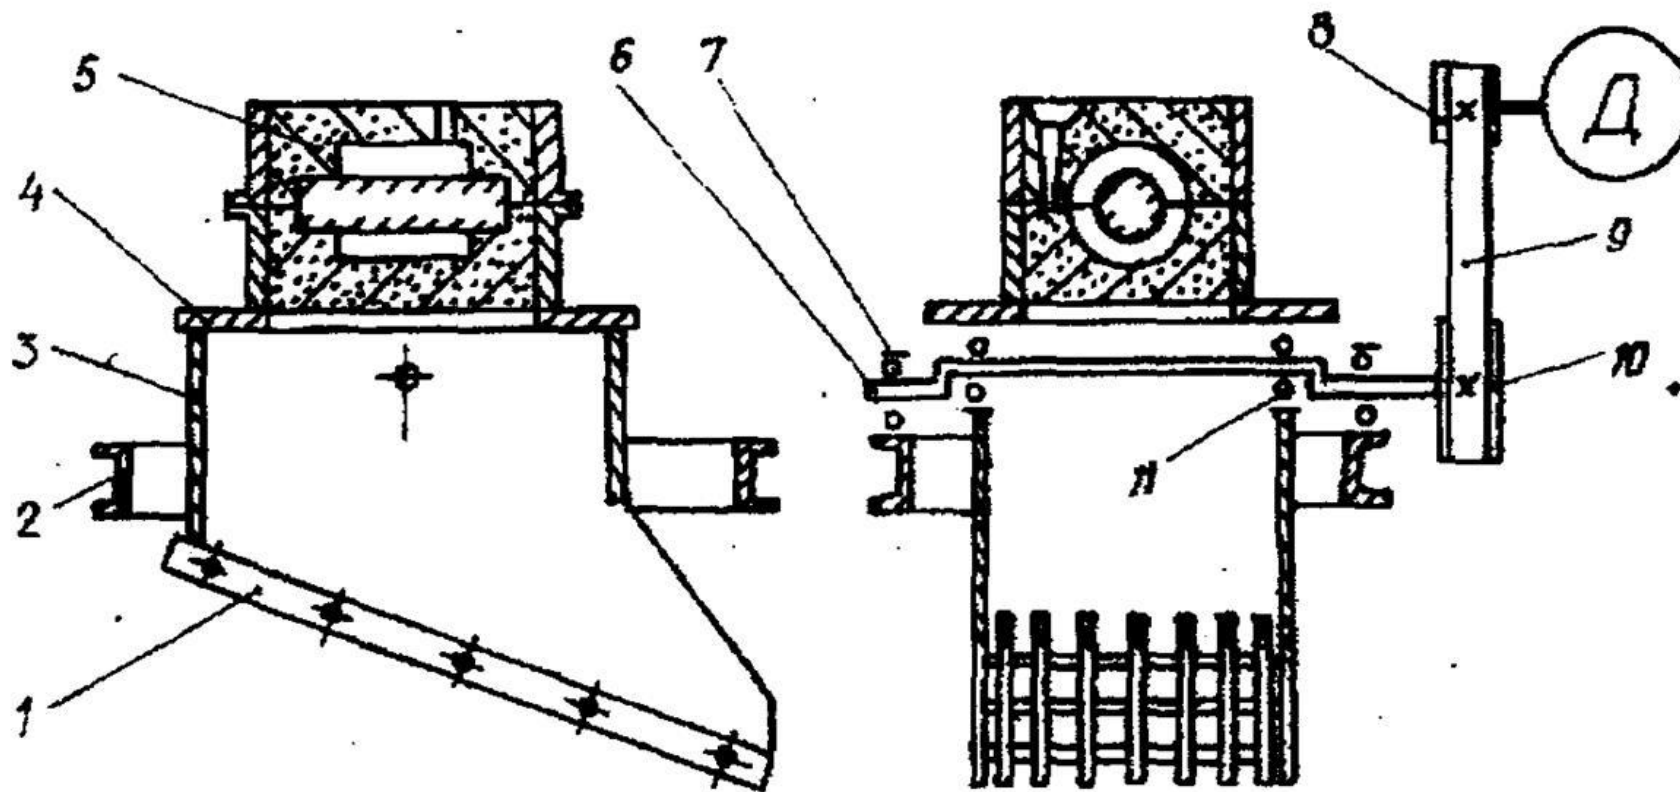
Схема вибивної машини: 1 – ґрати; 2 – рама нерухома; 3 – стінка; 4 – плита; 5 – форма; 6 – ексцентриковий вал; 7 – підшипник рами; 8, 10 – шків; 9 – пас; 11- підшипник вібраційного вузла.
